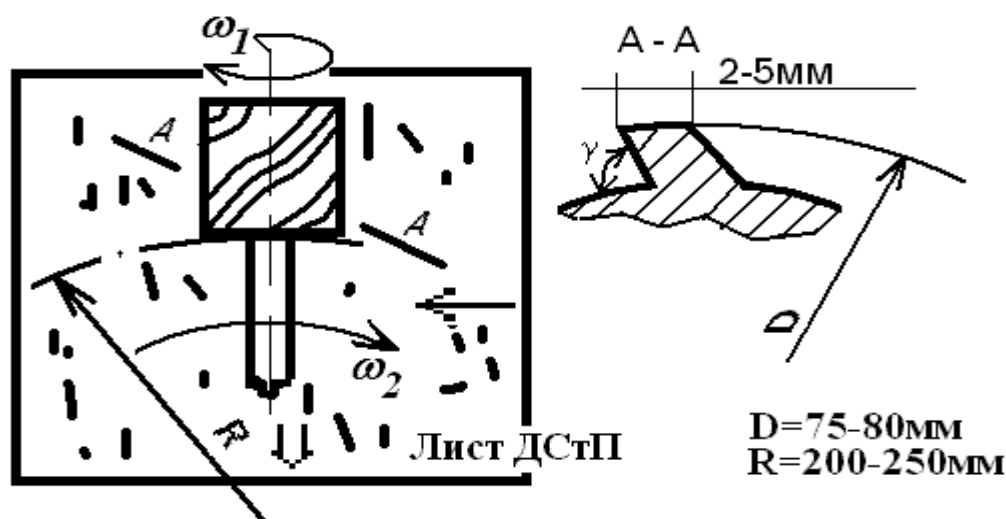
Схема фрезерования винтовой фрезой с двумя степенями свободы
